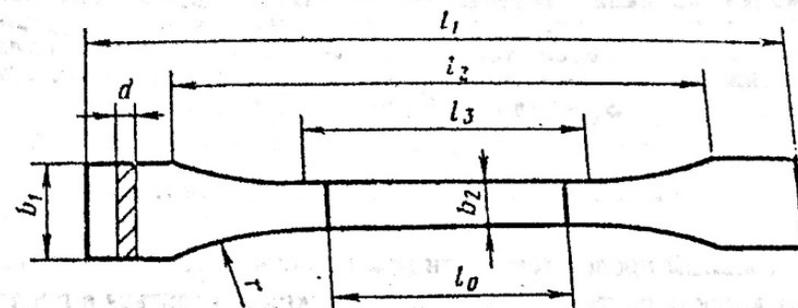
Образец для проведения испытаний полиэтилена на растяжение
